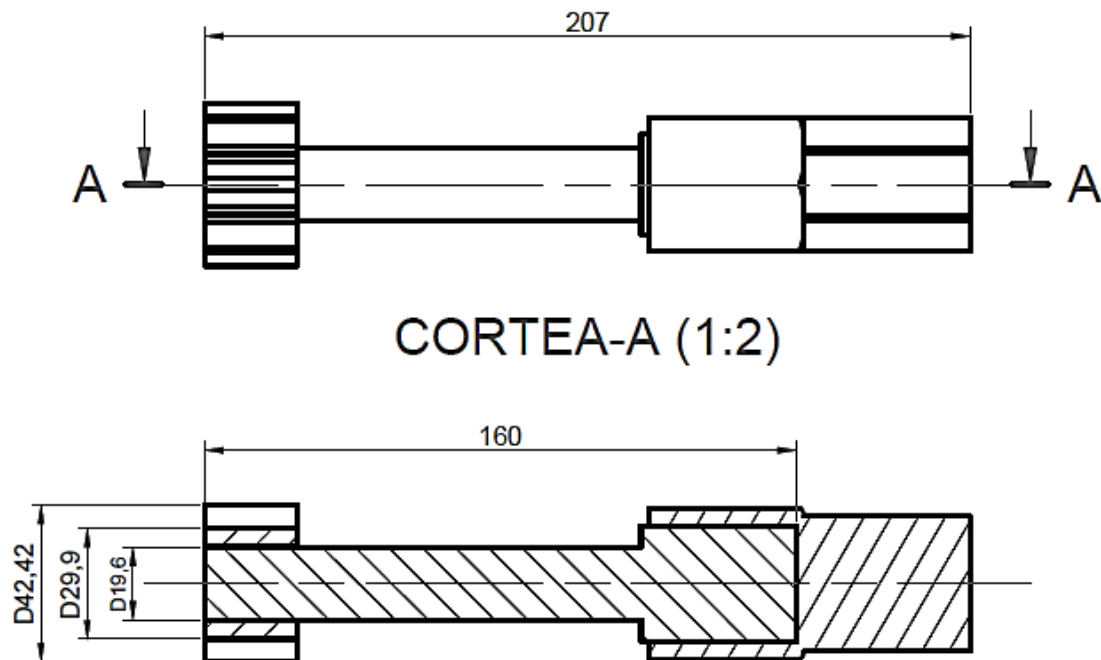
Vista frontal y corte del eje engranaje - manivela
